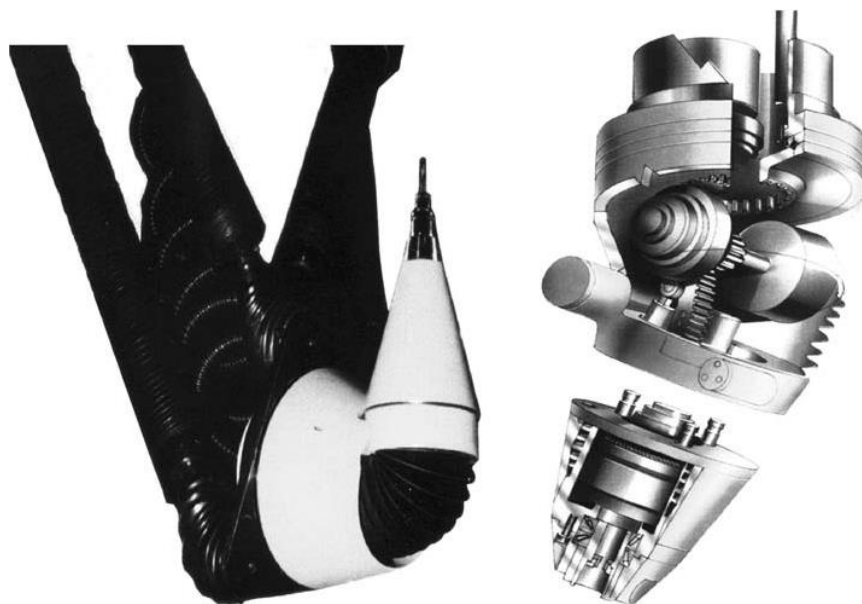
Поворотная головка конструкции «Geodetic»
